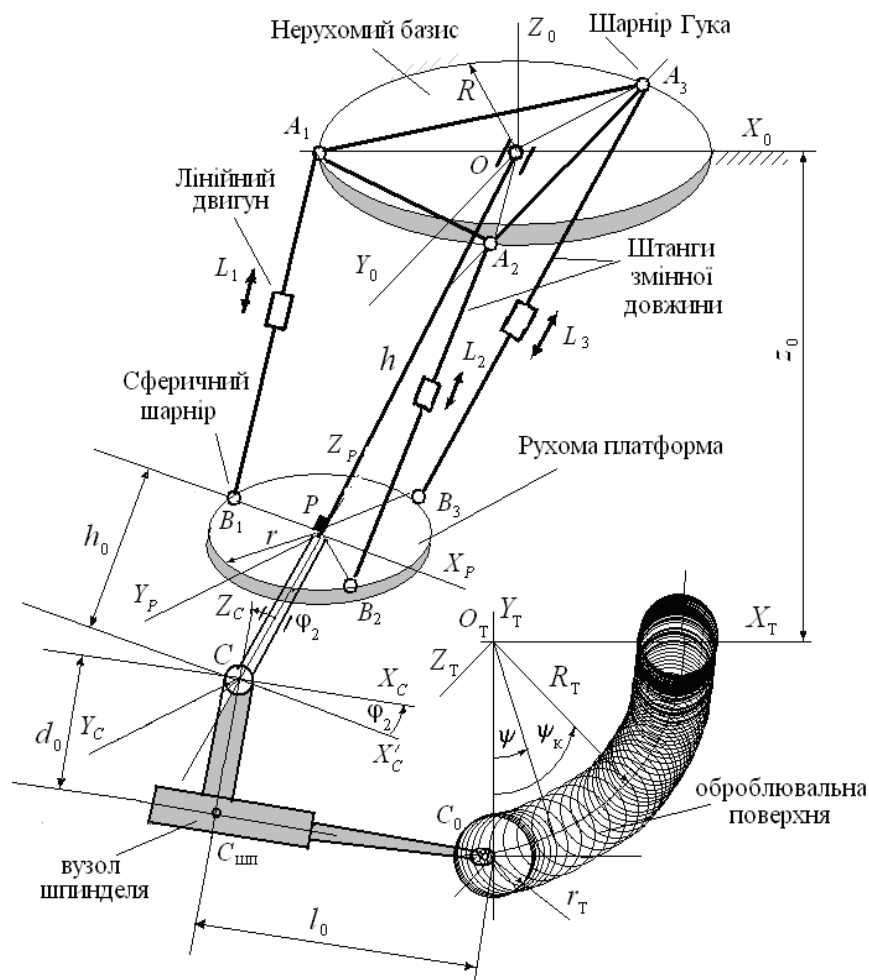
Розрахунково-кінематична схема механізму трицепта при обробці складної поверхні
